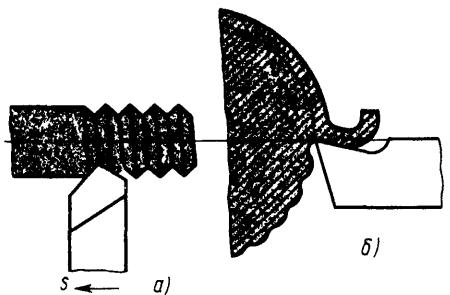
Образование поперечной (а) и продольной (б) шероховатости поверхности при токарной обработке
